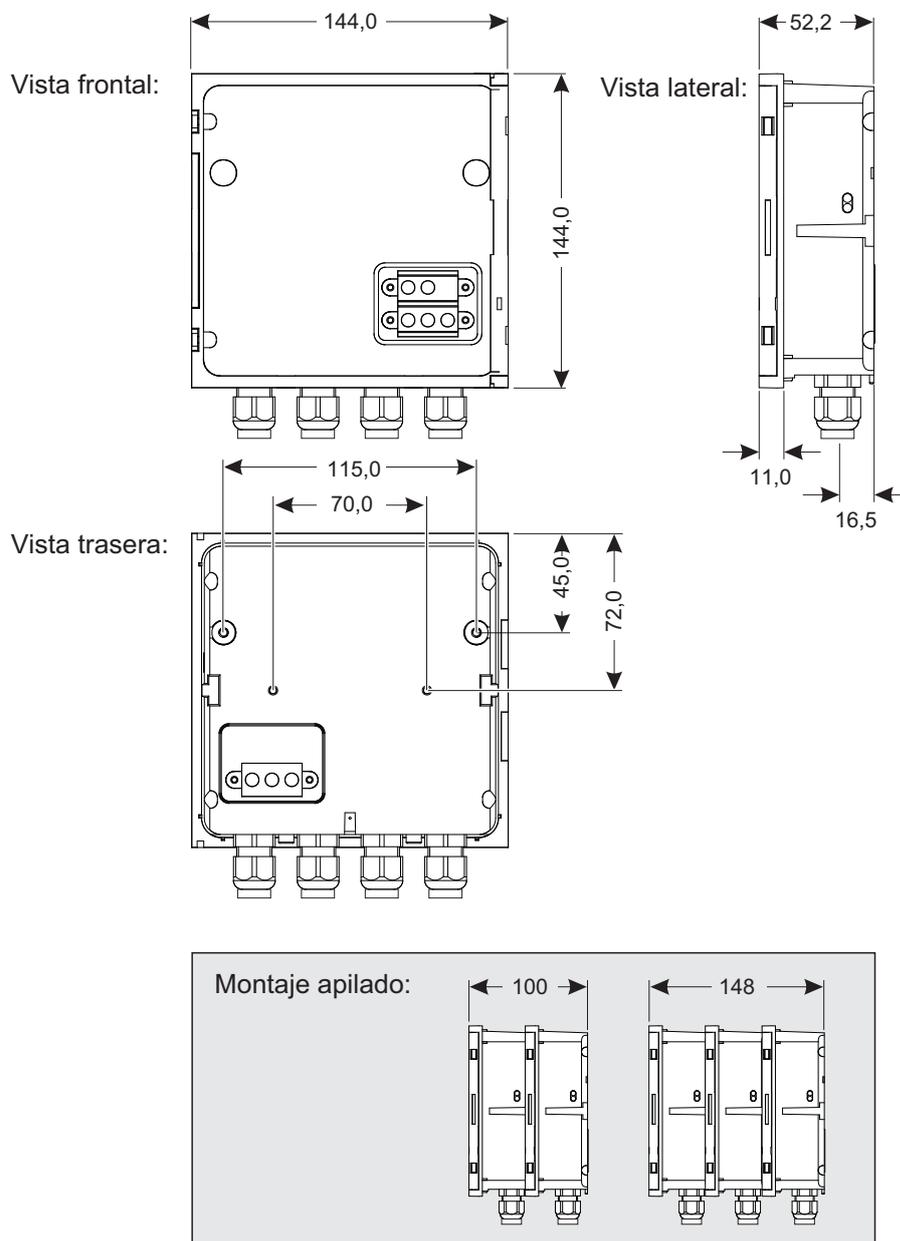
Dibujo acotado del módulo MIQ (dimensiones en mm)
